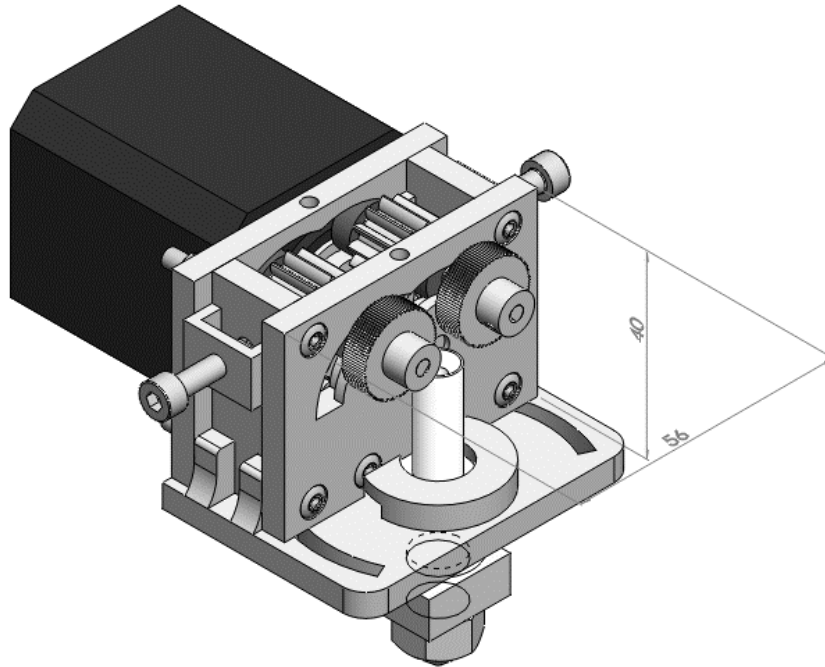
Extrusor de engranajes pivotantes (Versión 01)
